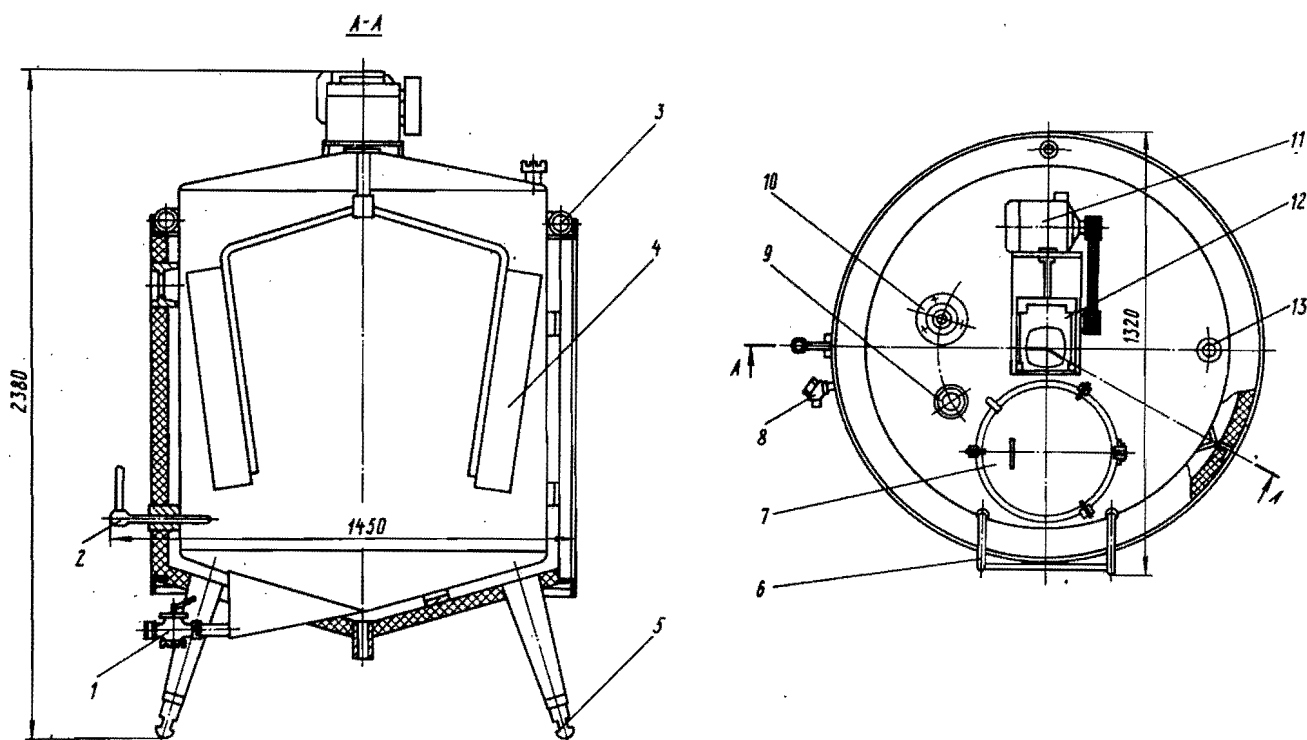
Общий вид резервуара сливоксозревательного марки РЗ-ОТН-1000:
